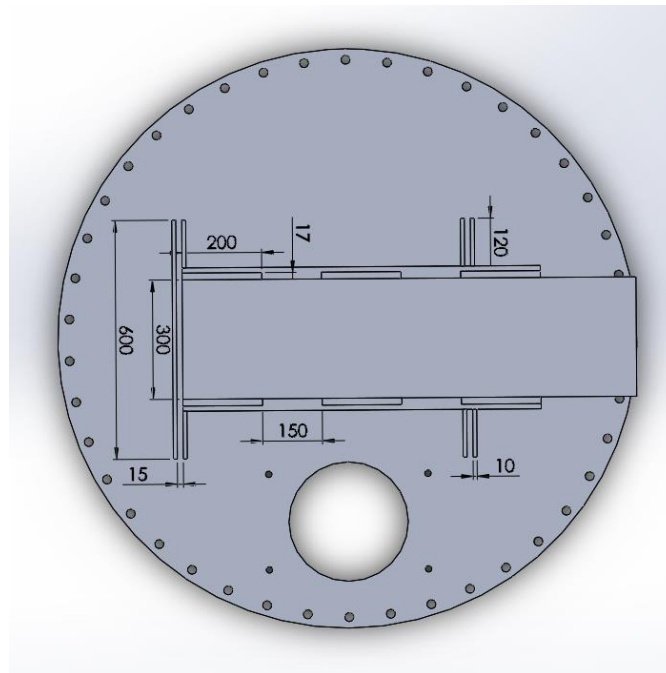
Dimensiones de la pluma sobre la placa y los cordones de soldadura.
